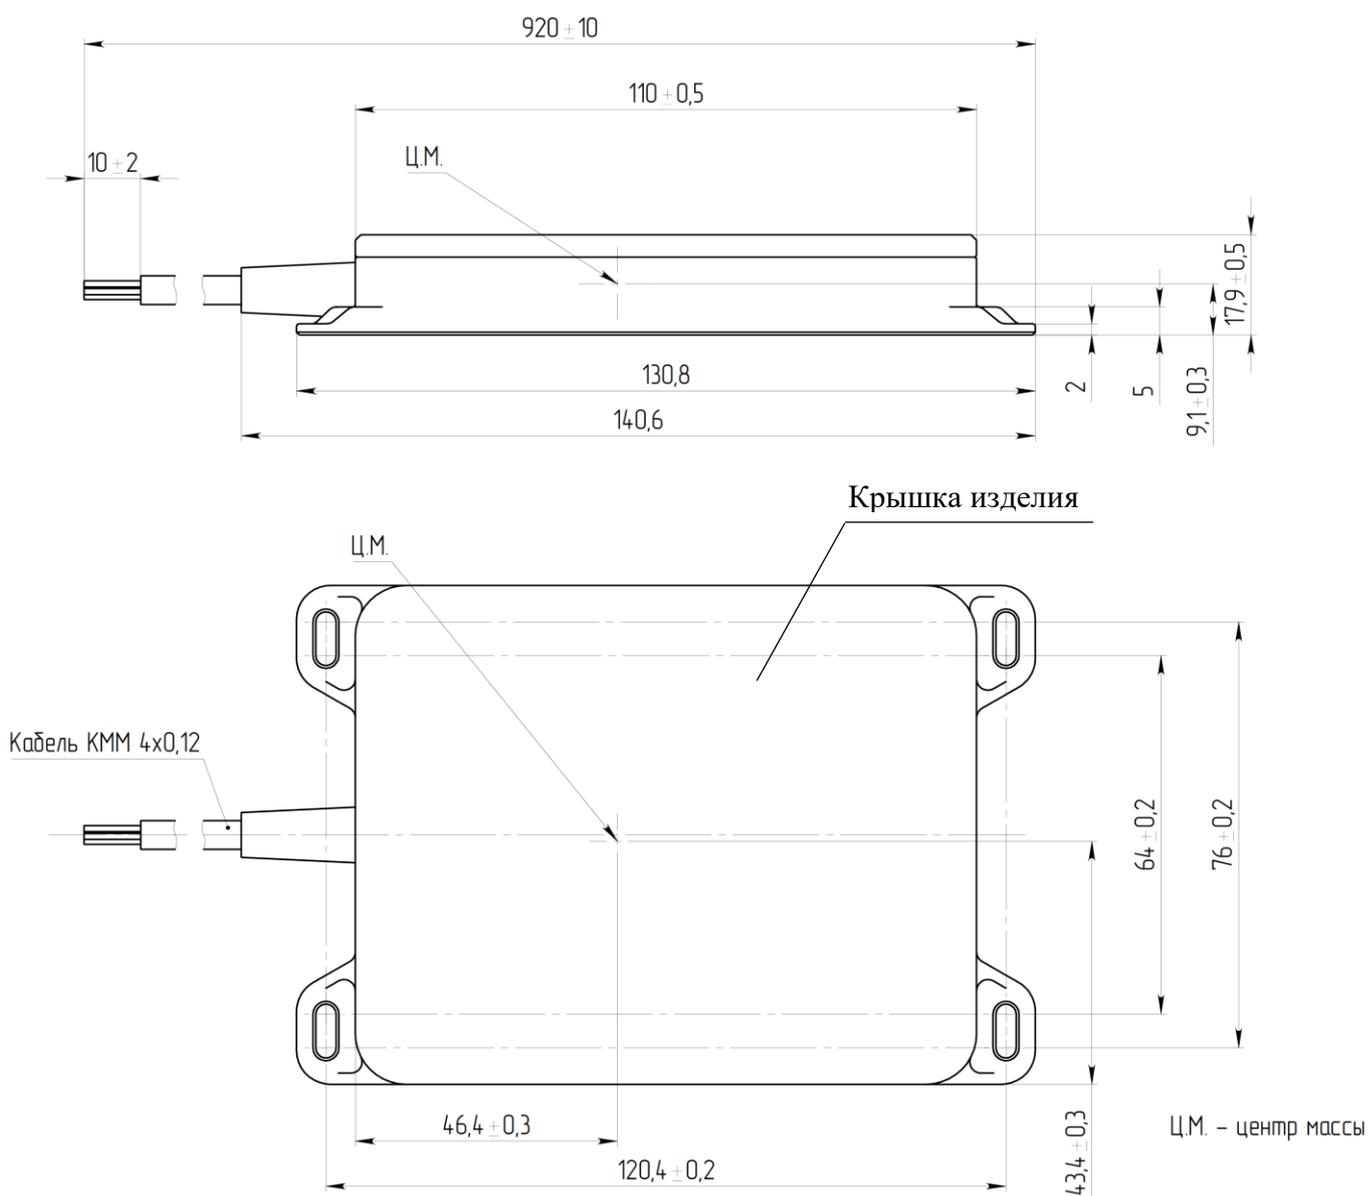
Габаритные размеры изделия, расположение отверстий для крепления (лист 1 из 2)
